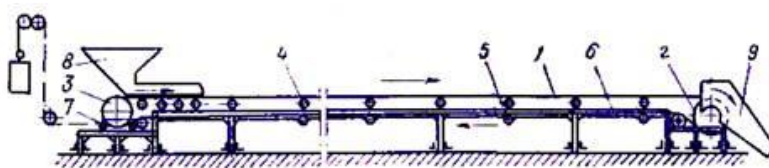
Схема стрічкового конвеєра: 1 – стрічка; 2 – приводний барабан; 3 – натяжний барабан; 4 – роликові опори; 5 – роликові опори пороژньої гілки; 6 – опорна рама; 7 – натяжний пристрій; 8 – завантажувальна воронка; 9 – розвантажувальний жолоб
